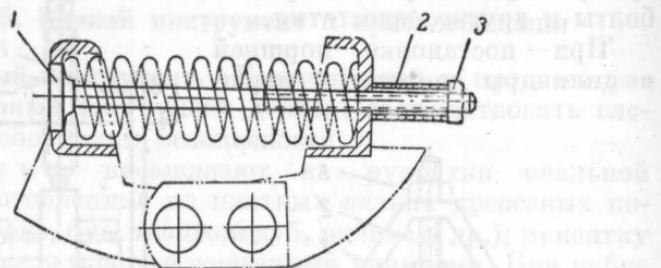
Приспособление для сжатия пружин бесшарнирных подвесок трактора ДТ-54:
